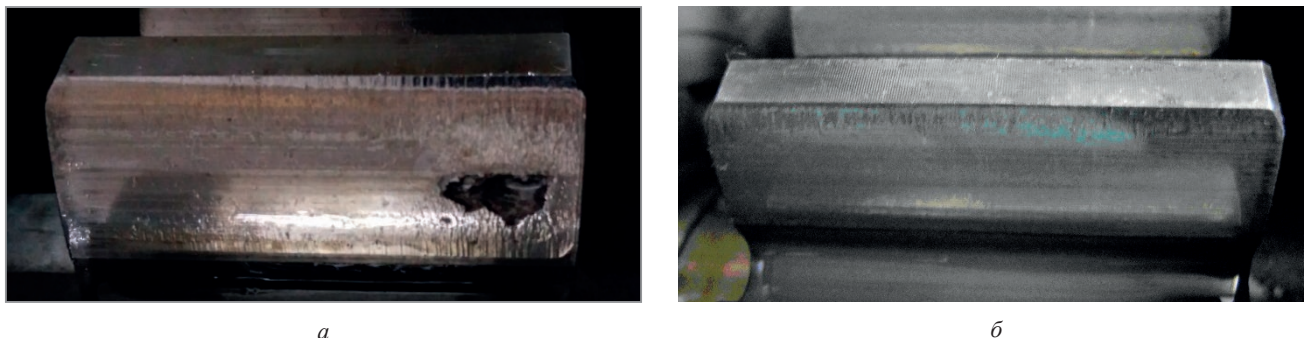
Состояние поверхностей зубьев после стендовых испытаний зубчатых колес из сталей:
